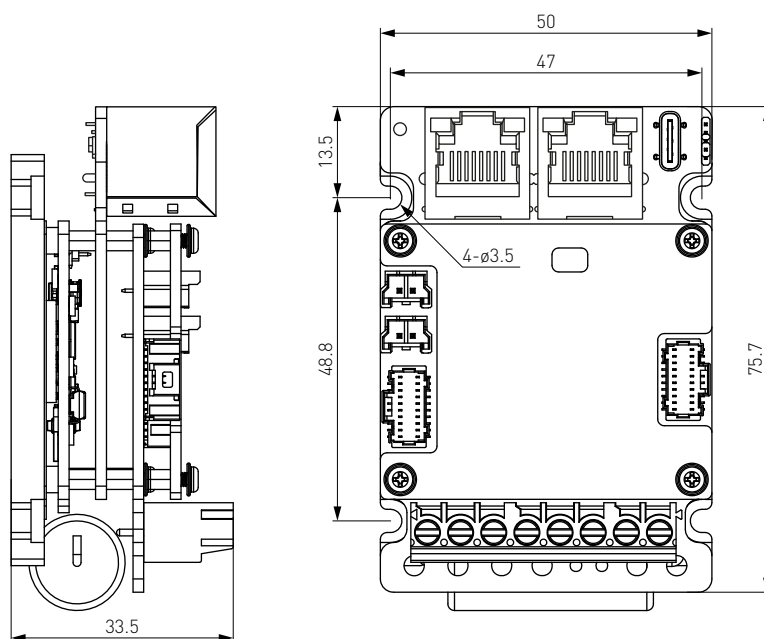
Габаритный чертеж серводрайверов ELD3-EC7001/7005/7010/7020BM (без корпуса).
